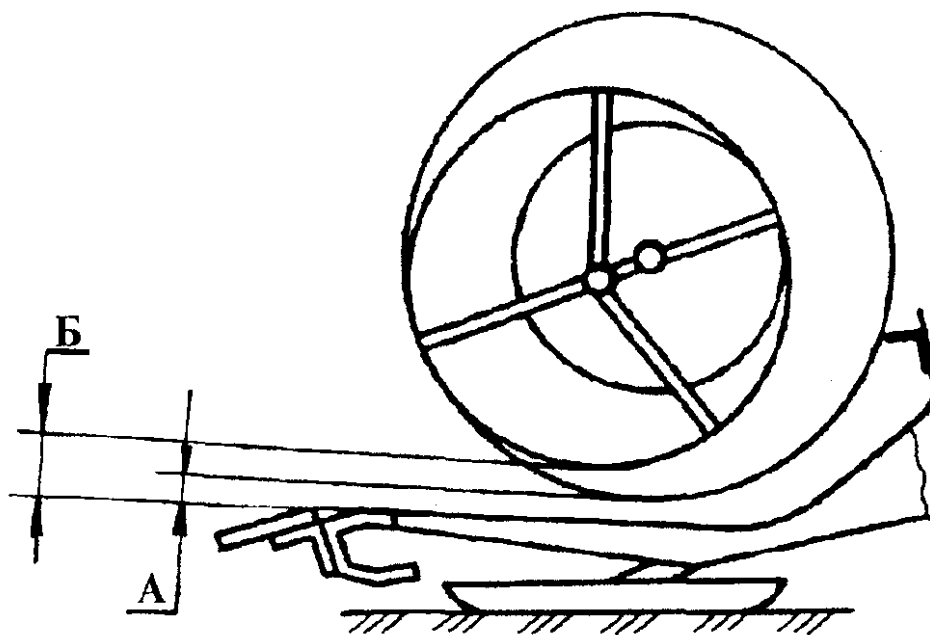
Схема расположения шнека и его пальчикового механизма при работе жатки: А – зазор между спиралью шнека и днищем корпуса; Б – зазор между пальцами пальчикового механизма и днищем корпуса
